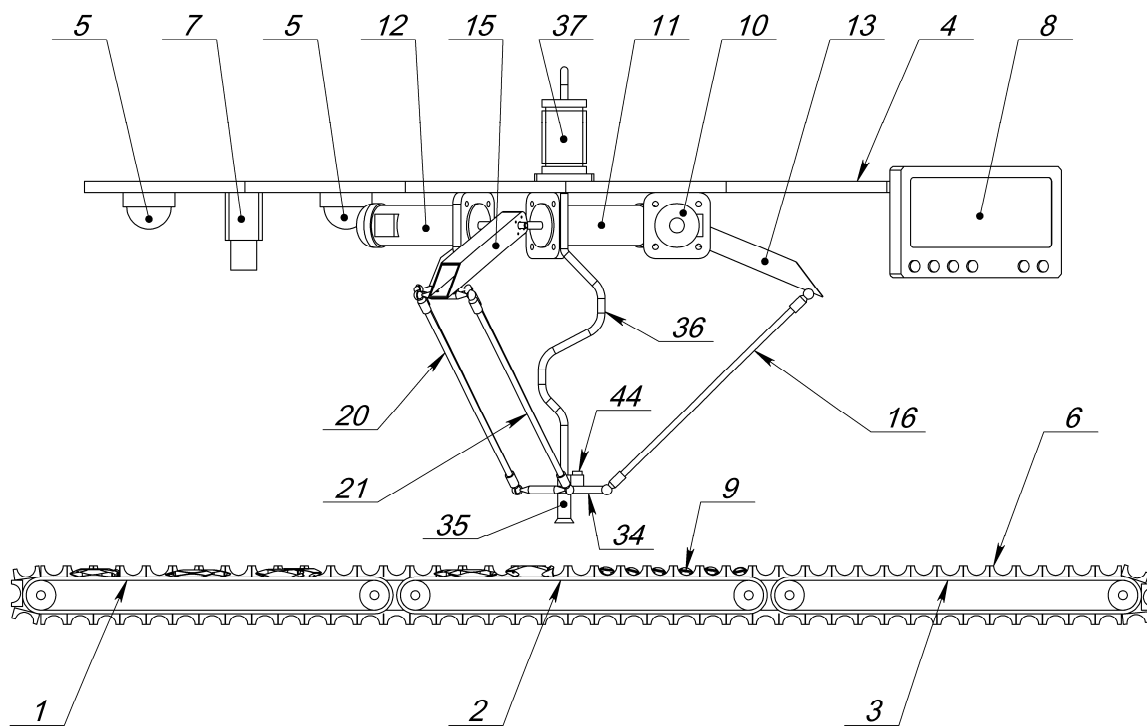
Предлагаемое устройство для загрузки рыбы в рыбообрабатывающие машины, вид слева
